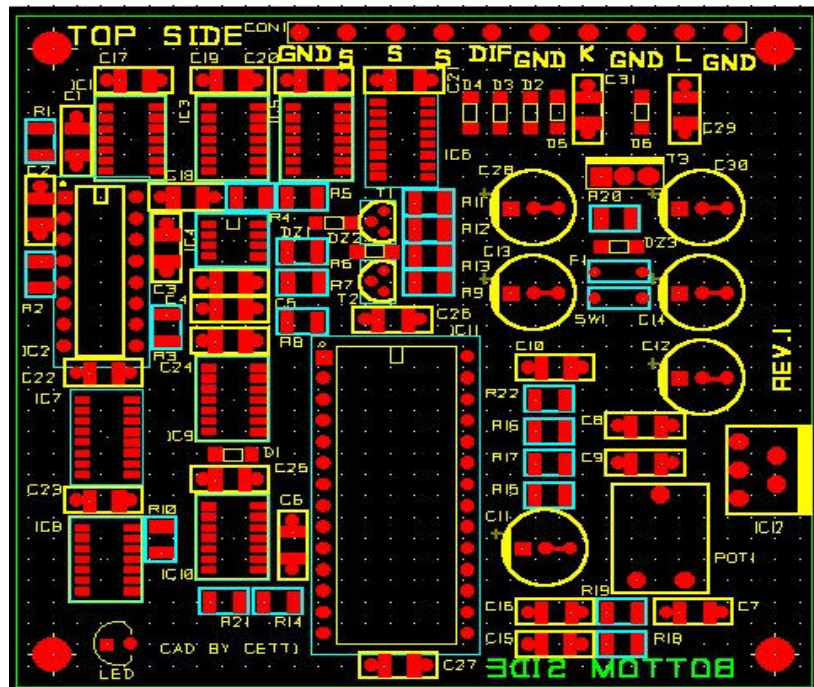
Placă realizată într-un sistem PCB, cu componentele plasate
